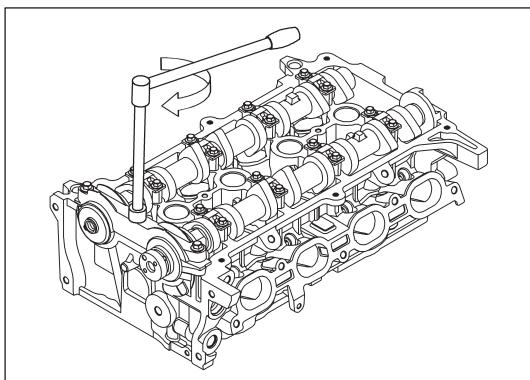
Установка крышек подшипников распределительного вала с передней стороны
